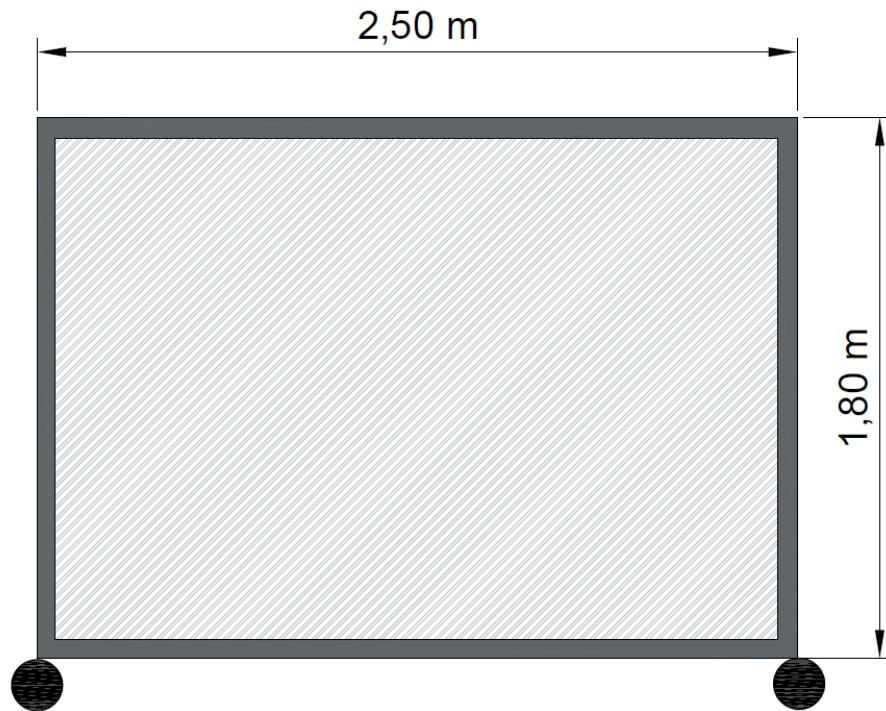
Vista frontal del apantallamiento térmico corredizo para la zona de puente grúa de la propuesta 2
